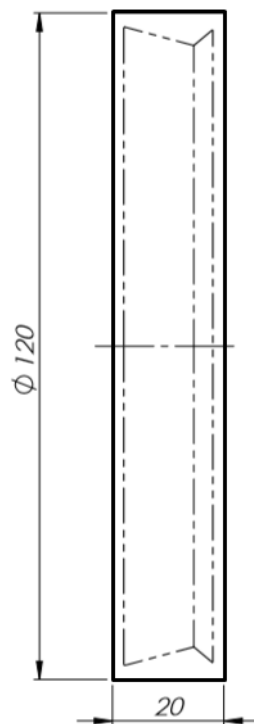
Ескіз заготовки деталі «Фреза»
